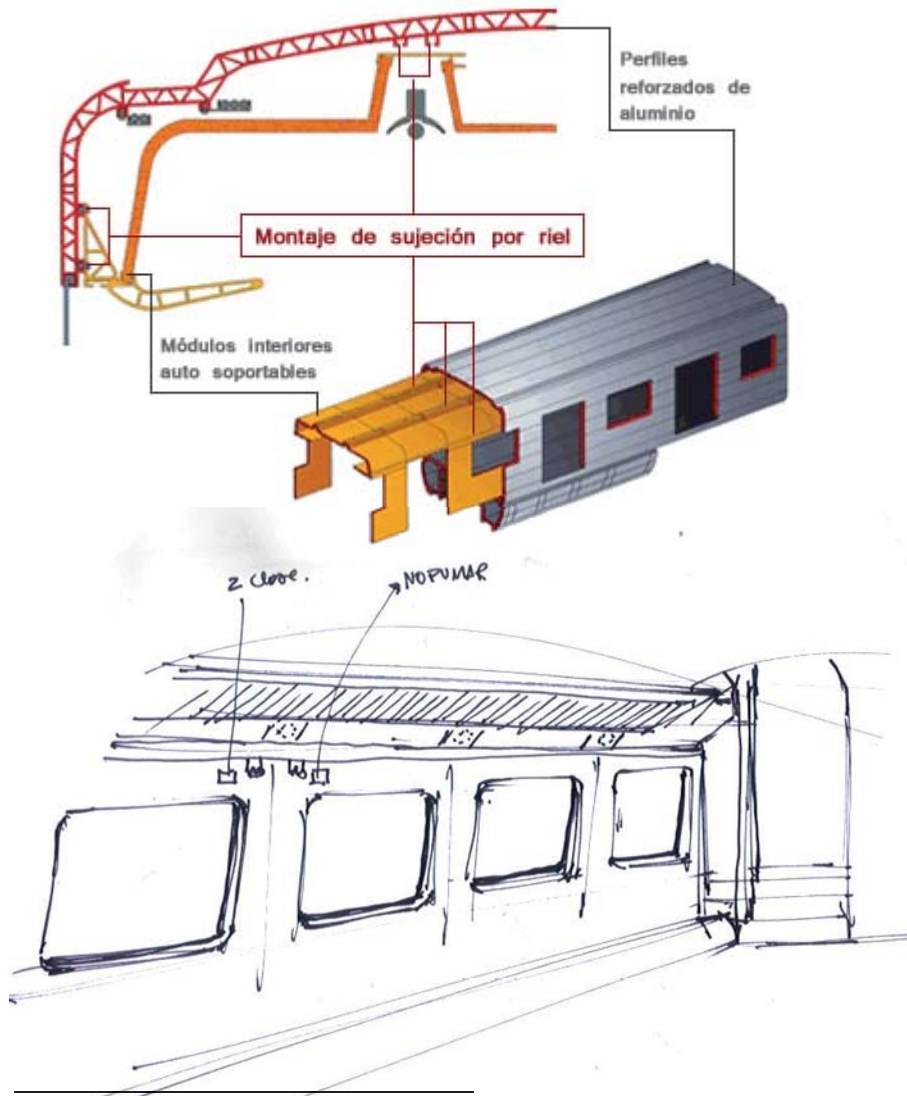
Sistema de unión de los paneles interiores a la estructura de aluminio.
